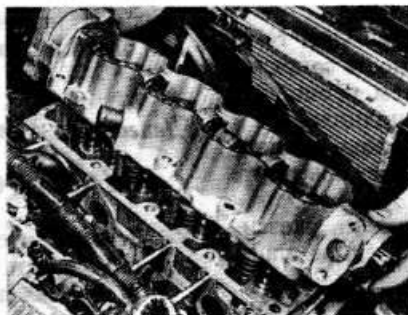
Отделение корпуса распредвала от головки блока цилиндров — двигатель 1,6 л с многоточечным впрыскиванием топлива
